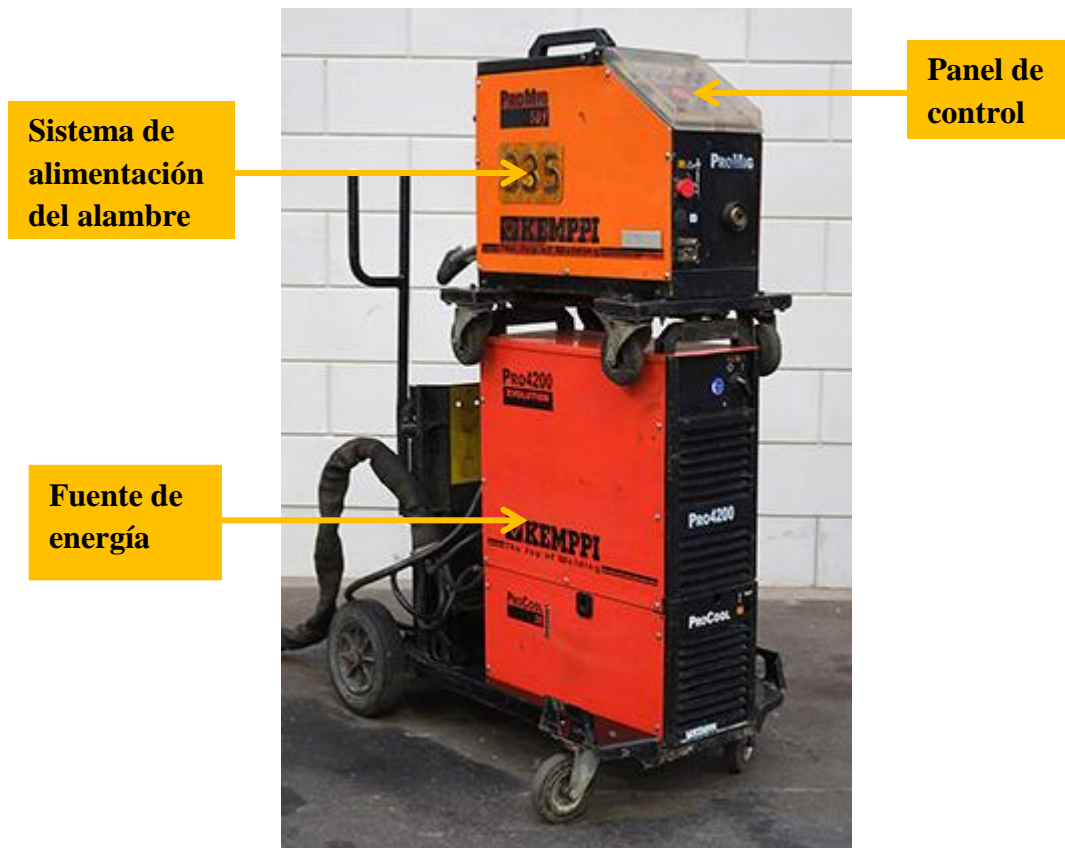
FUENTE DE SOLDADURA UTILIZADA EN LA EMPRESA.
